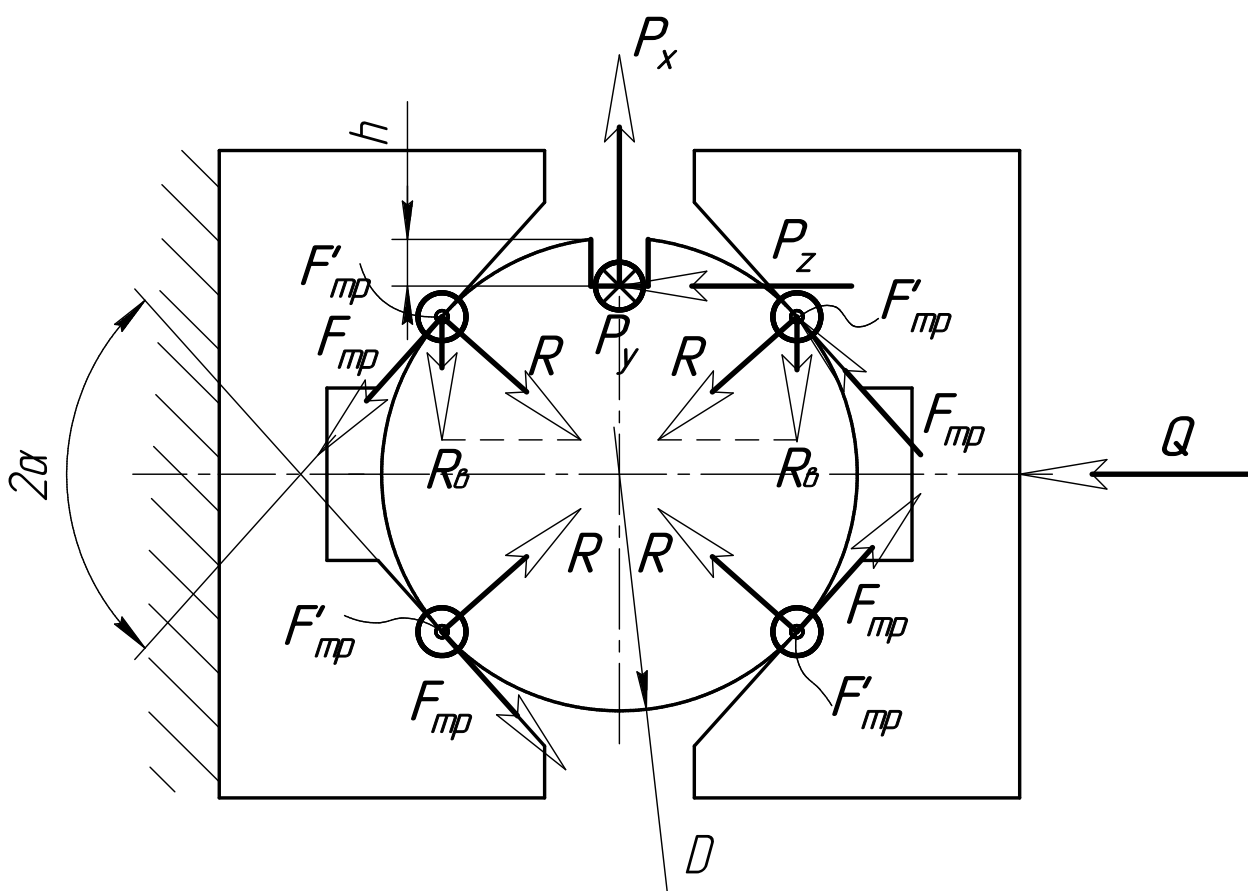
Розрахункова схема для визначення зусилля закріплення деталі при фрезеруванні шпонкового пазу кінцевою фрезою
